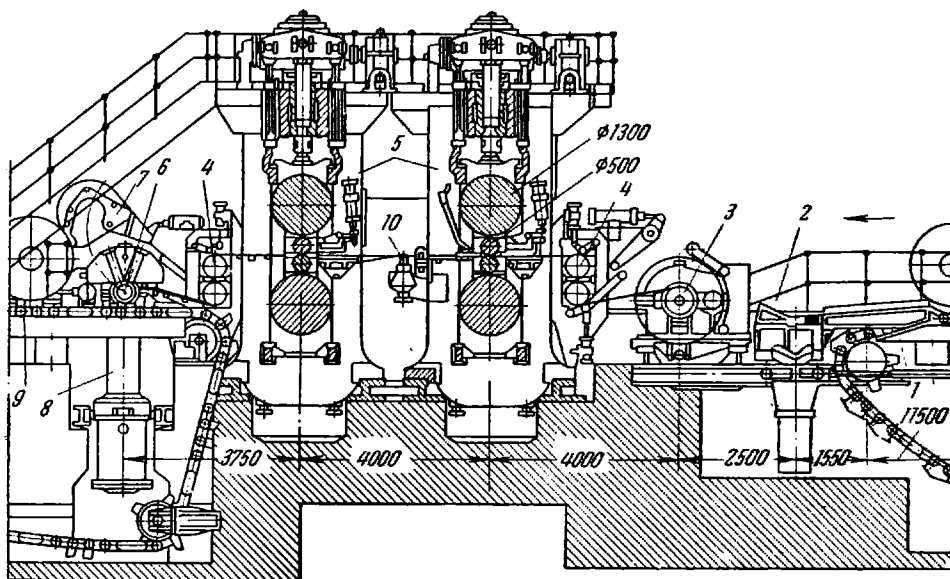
Двухклетевой дрессировочный стан 500/1300×1200 для жести
